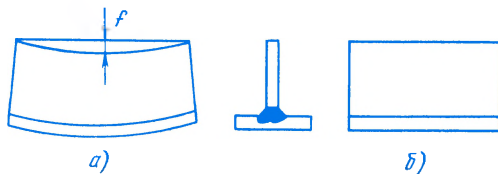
Обратный выгиб элементов тавра: а – сборка тавра с обратным выгибом, б – форма тавра после сварки
